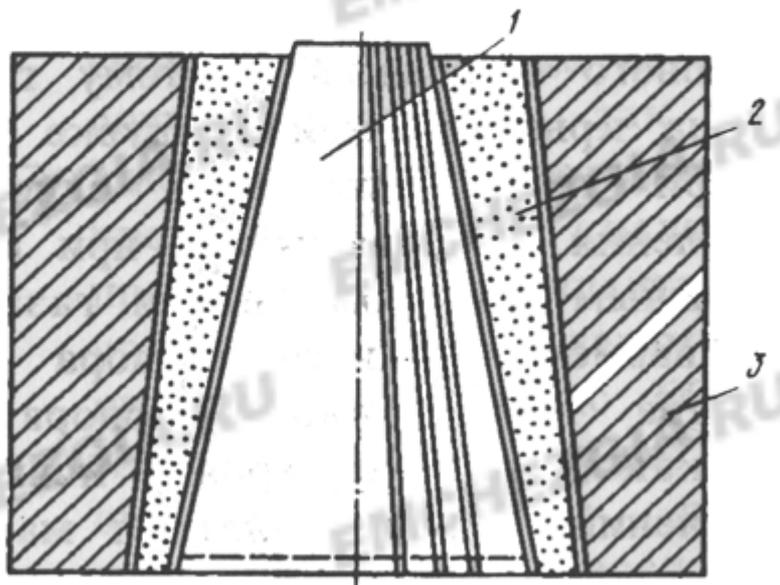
Конструкция пористой пробки (вставки) для продувки стали аргоном: 1 — вставка с каналами для прохода газов; 2 — огнеупорный корпус; 3 — гнездовой кирпич
